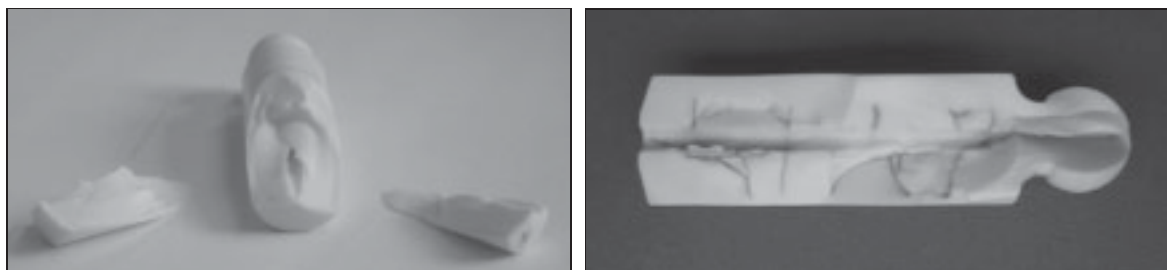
Proof-Test mit as-fired-ZrO₂-Kolben: Bruchbild (links) und Rissbild mit Farbeindringverfahren nach Innendruckprüfung (rechts).
